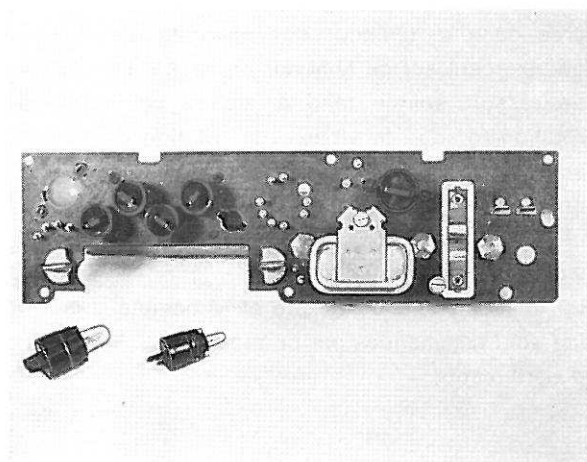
Plaque de montage des indicateurs et des lampes témoins, derrière
